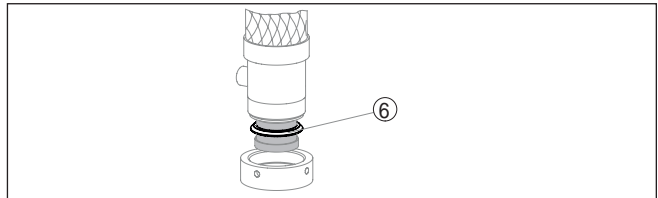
Kit de montagem - Mangueira de refrigeração do cintilador - em baixo
